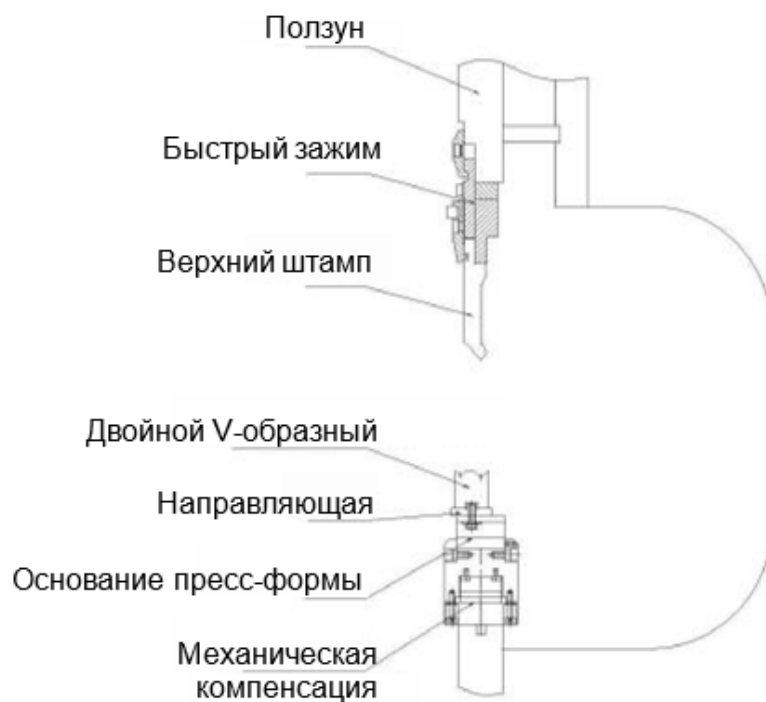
Установка и регулировка двойного V-образного концентрического штампа
